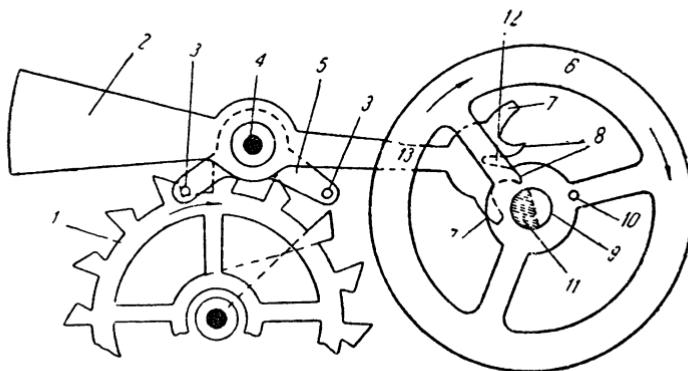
Схема работы комбината баланса и спуска: 1—анкерное колесо; 2—противовес; 3—входной и выходной штифты; 4—ось вилки; 5—скобка; 6—балансовое колесо; 7—усики вилки; 8— рожки вилки; 9—паз оси; 10—эллипс; 11—ось баланса; 12—паз вилки; 13—изогнутая часть вилки
